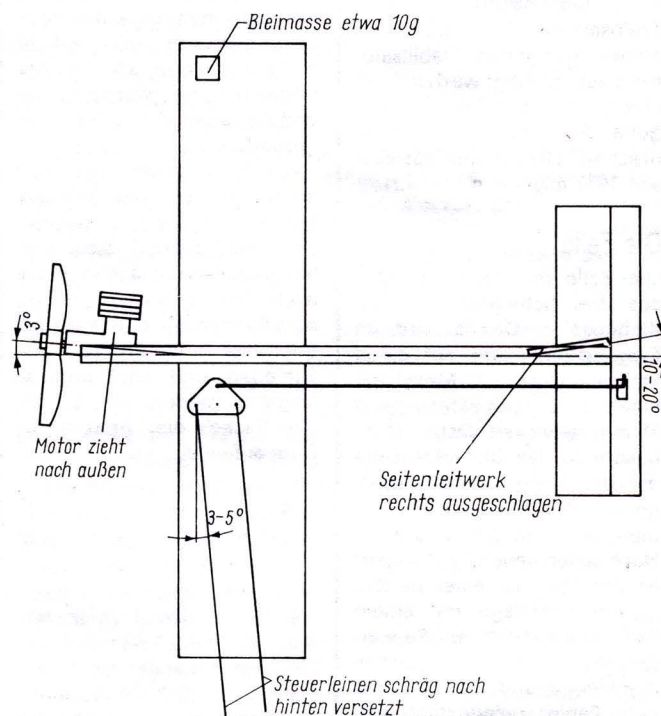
Die Zugkraft der Steuerleinen wird erhöht ▲
